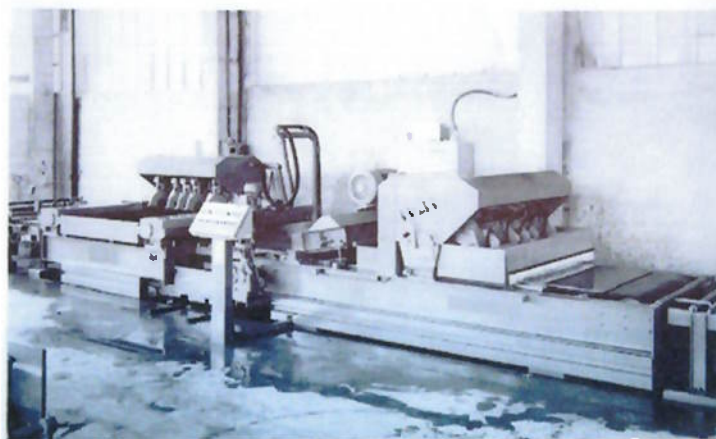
Serragem longitudinal e transversal das chapas.
